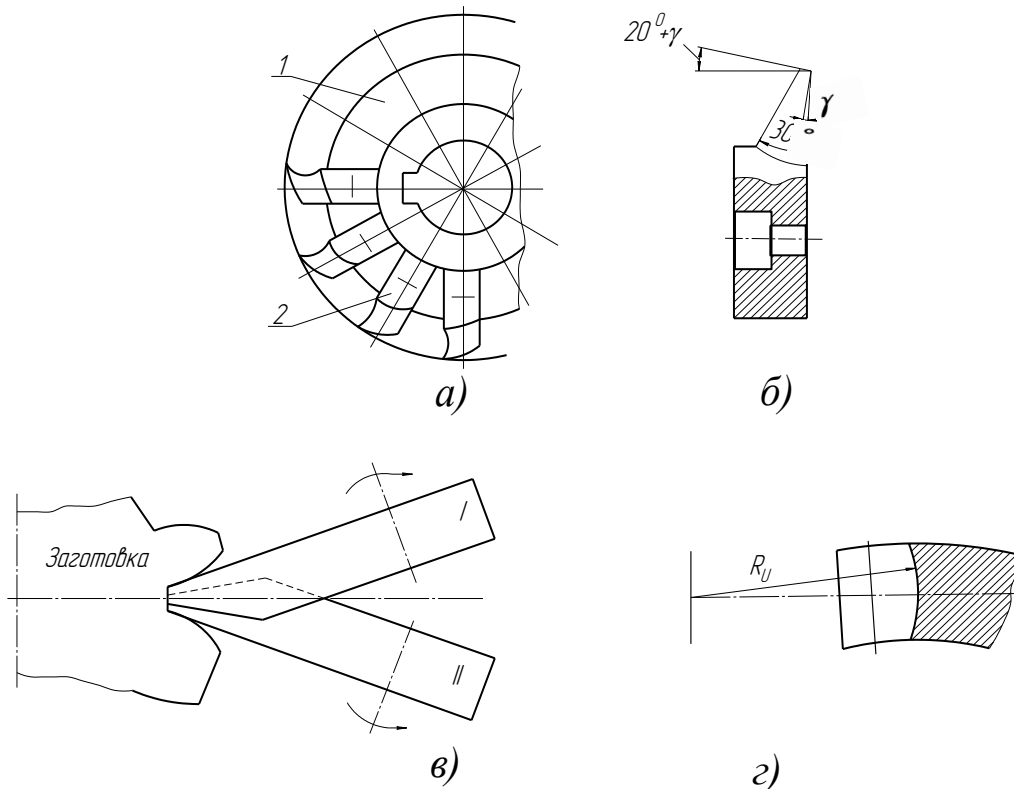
Схема обробки двома дисковими фрезами
